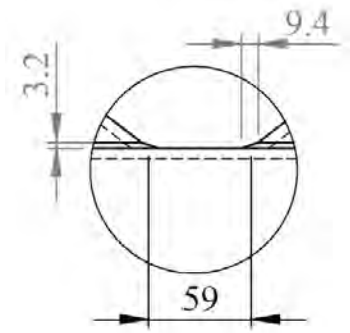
Detalle del cordón de la soldadura.
